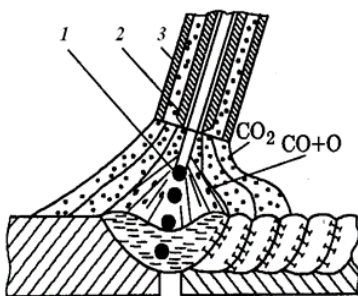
Схема процесса дуговой сварки в углекислом газе
